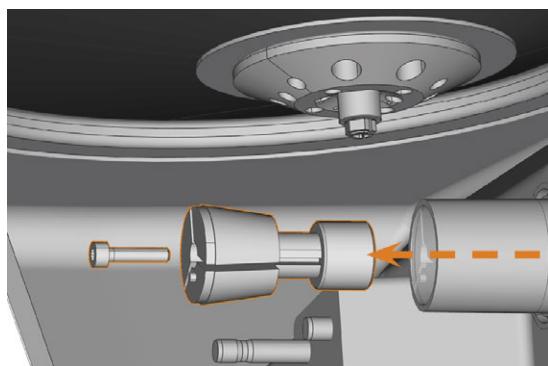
RETIRER LA PINCE DE SERRAGE DU SUPPORT DE PIÈCES BRUTES
